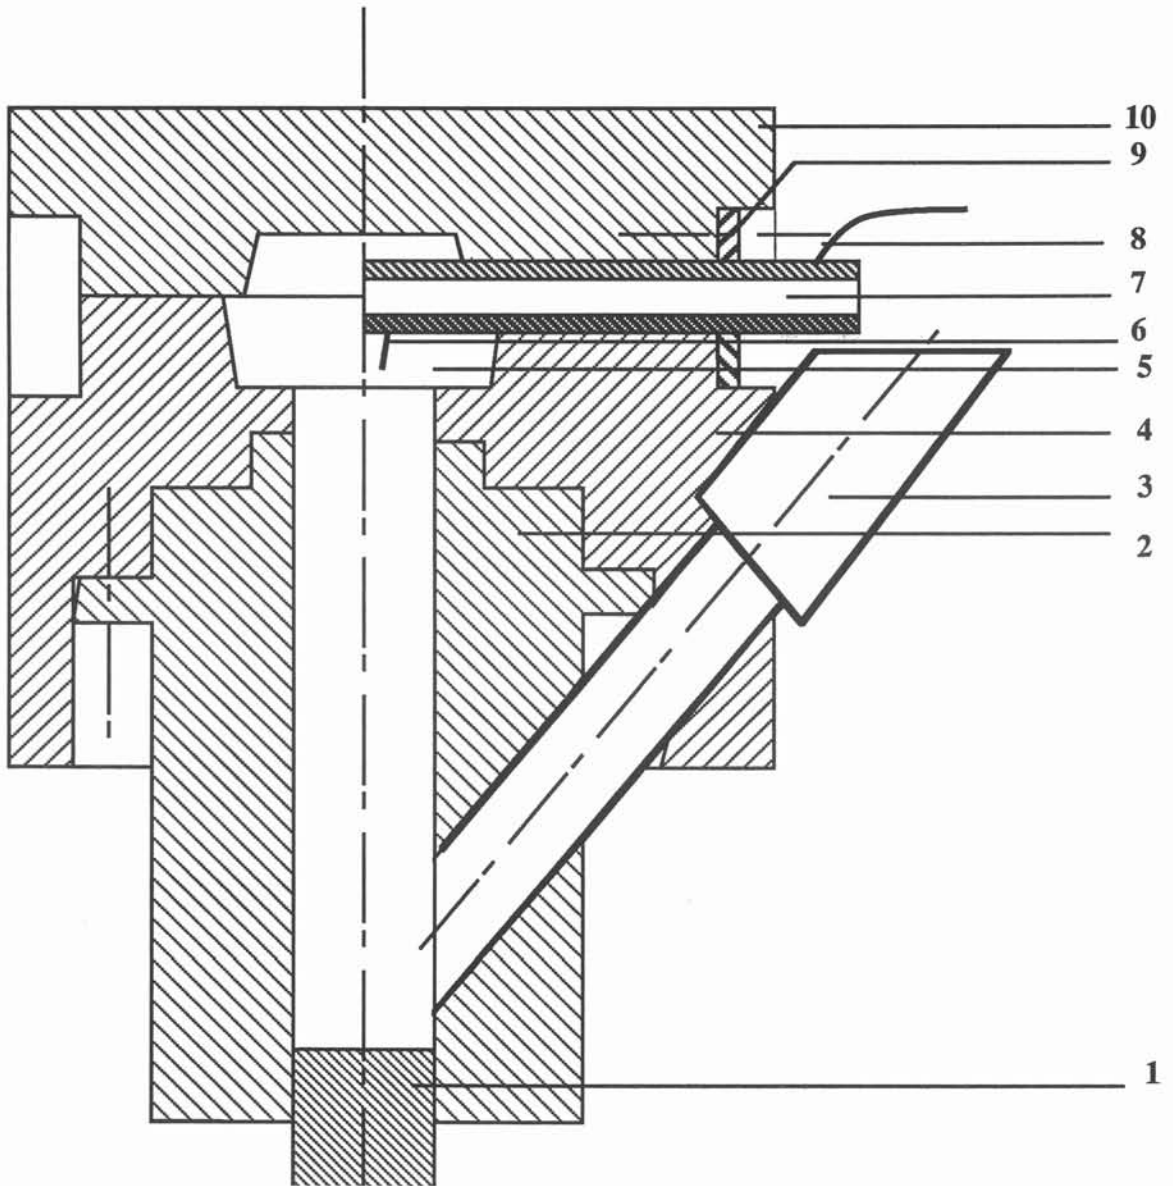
Schéma de la chambre d'injection et du tube moule
